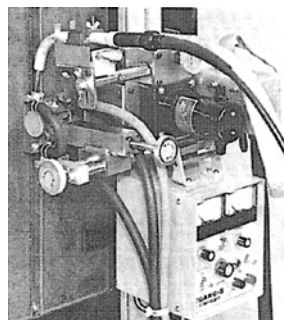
溶接材料メーカーが市販を始めた簡易立向自動溶接装置
